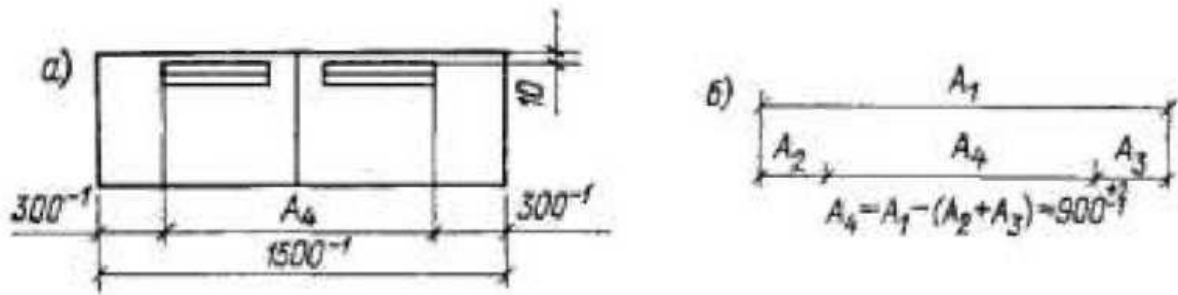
Схема сварного изделия (а) и его размерной цепи (б)
